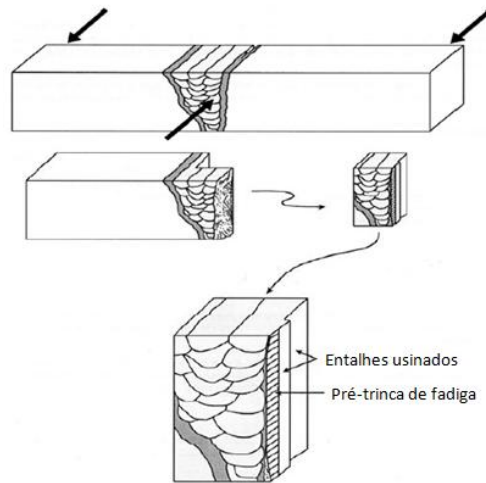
Desenho esquemático do seccionamento de uma junta soldada (FERNANDES, 2011).
